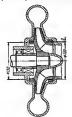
Rotor de filabes con fuerza axial de presión hidrosstática equili-
